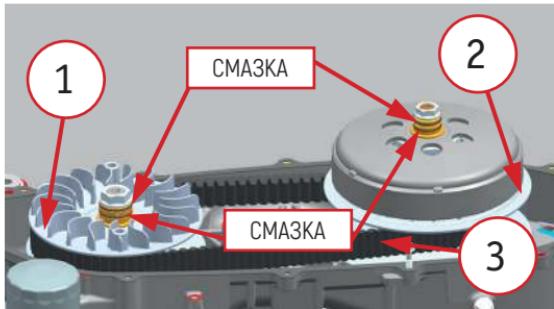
Места смазки передаточного механизма: 1 – ведущий шкив; 2 – ведомый шкив; 3 – клиновой ремень.
